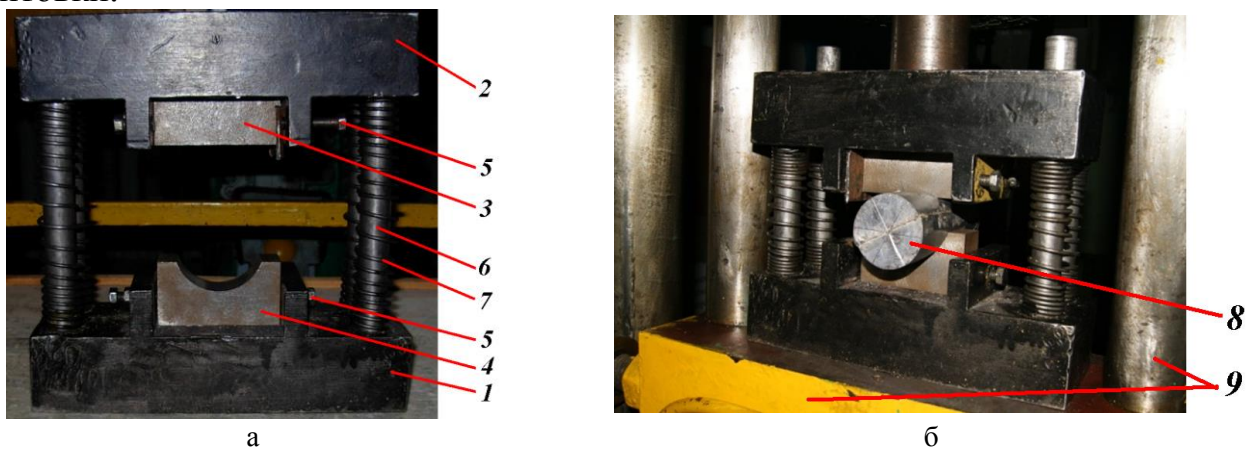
Универсальная испытательная машина: а – штамповый блок для исследования; б –: протяжки заготовок; 1 и 2 – нижняя и верхняя плиты; 3 и 4 – верхний плоский и нижний вырезной бойки; 5 – крепёж; 6 и 7 – направляющие и пружины; 8 – образец; 9 – испытательная машина
